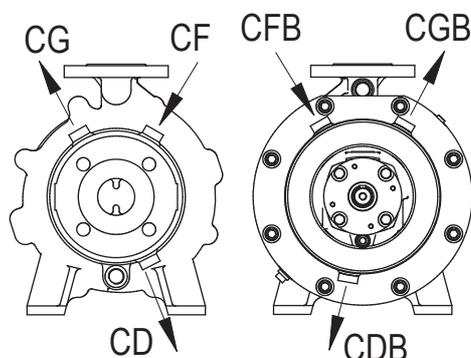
Соединения кожуха корпуса насоса и кожуха консольной опоры подшипника.
